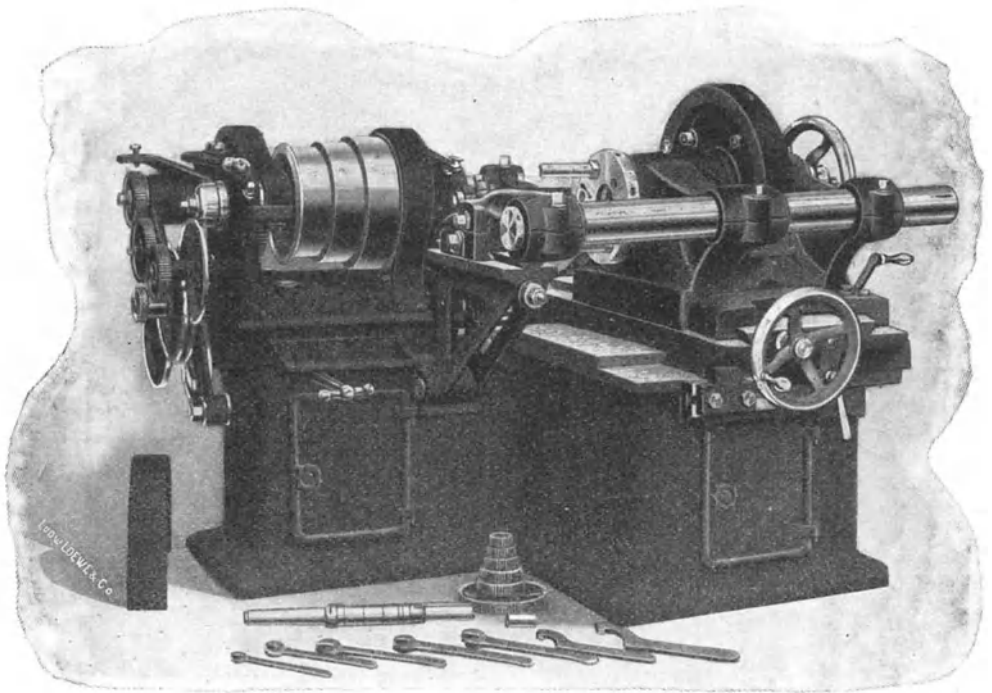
Die Rundfräsmaschine von L. Löwe & Co.
